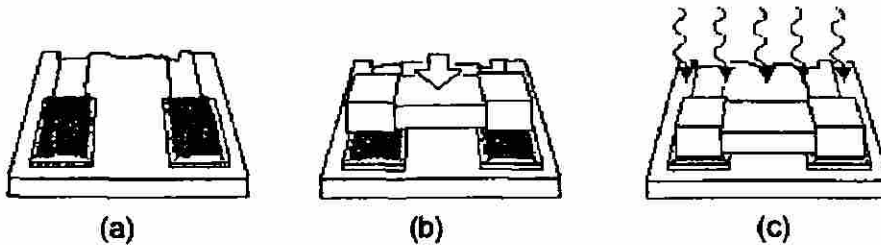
Proceso de SMT: (a) colocación de soldadura de pasta, (b) colocación de componente, (c) al horno de reflujo.
